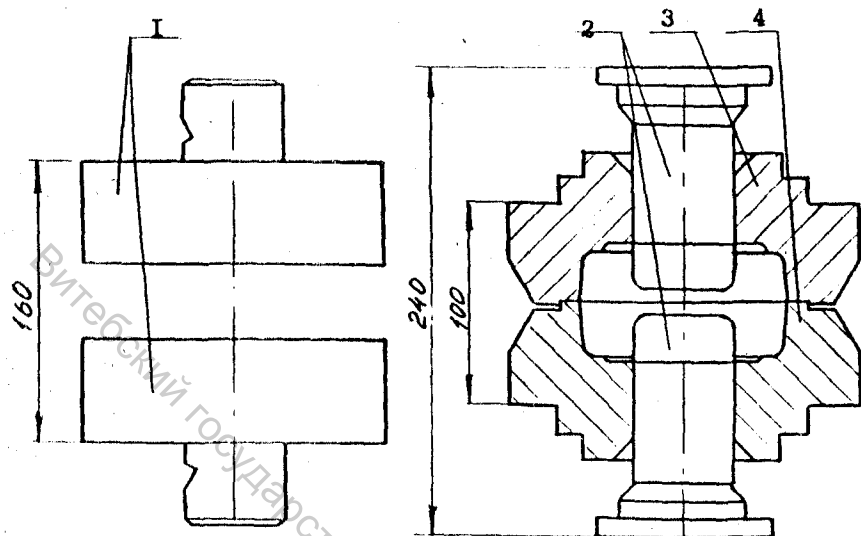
Рабочие части штампов для безоблойной двусторонней штамповки поковки дифференциала.
